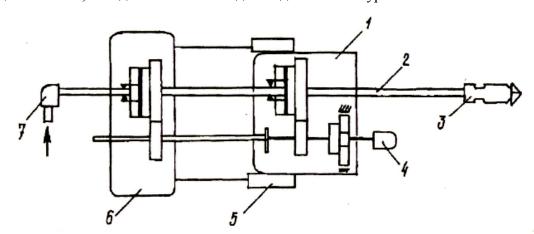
Принципиальная схема конструкции станка НКР -100:
